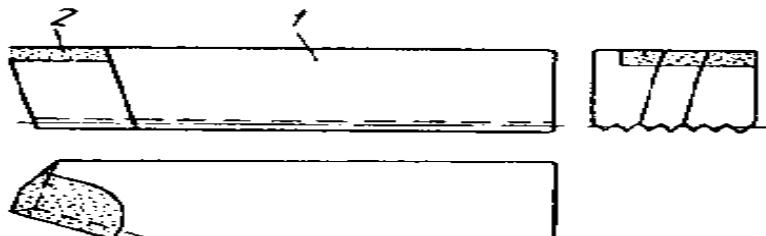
Різець торцевої фрези з напайною пластиною з твердого сплаву (1 – державка різця; 2 – пластина твердого сплаву)
